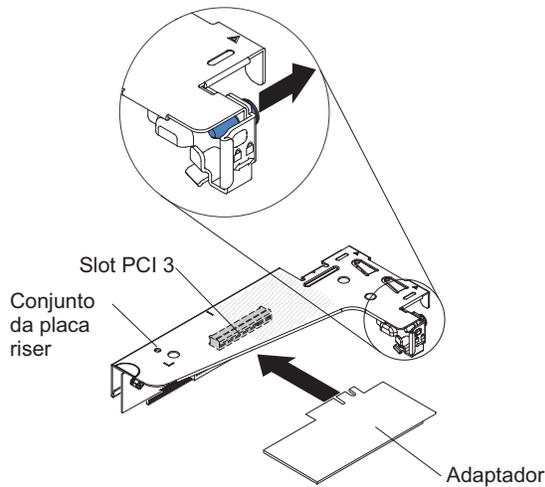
Remoção do Adaptador do Conjunto da Placa Riser PCI 2
